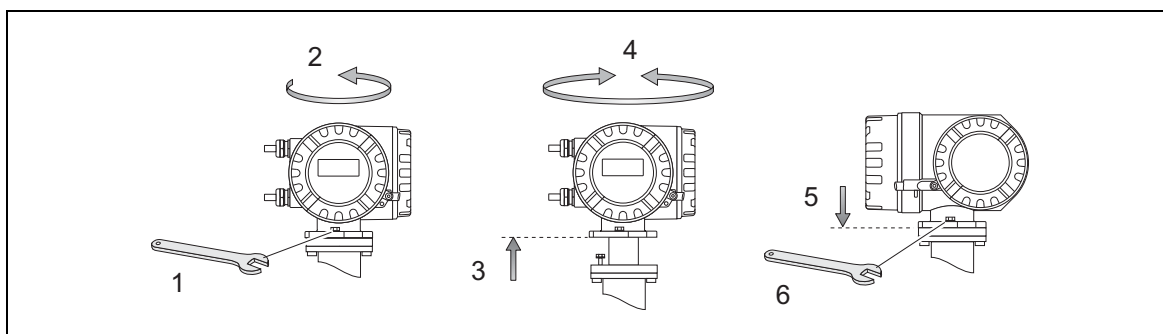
Поворот корпуса преобразователя (в алюминиевом рабочем корпусе)
